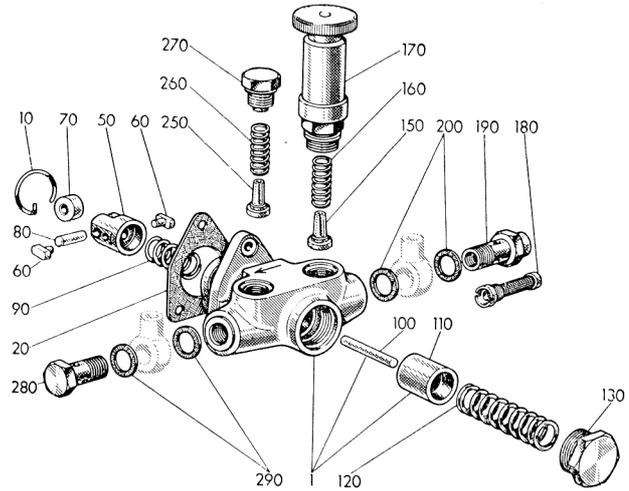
Vue éclatée de la pompe d'alimentation en combustible.
